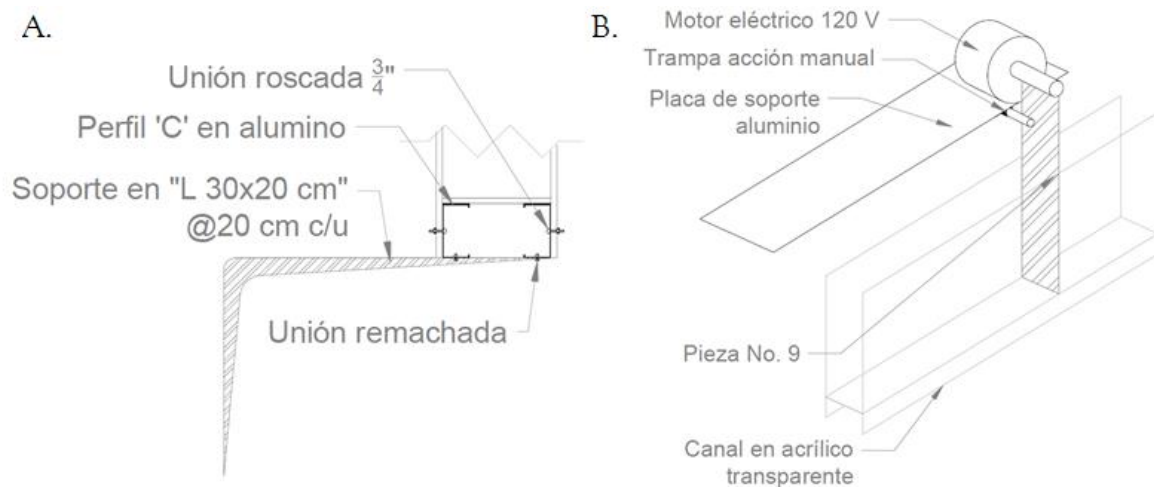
Detalles del montaje del canal Collaptes V1.0: A. Detalles de conexión entre el canal y los soportes, B.
